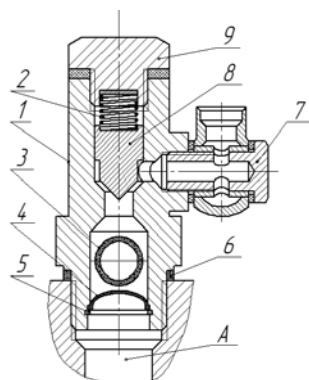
Воздушный клапан: 1 – корпус; 2 – пружина; 3 – поплавковый клапан; 4 – сетка; 5 – стопорное кольцо; 6 – уплотнительная прокладка; 7 – отводящий штуцер; 8 – игла; 9 – болт; А – внутренняя полость фильтра тонкой очистки
